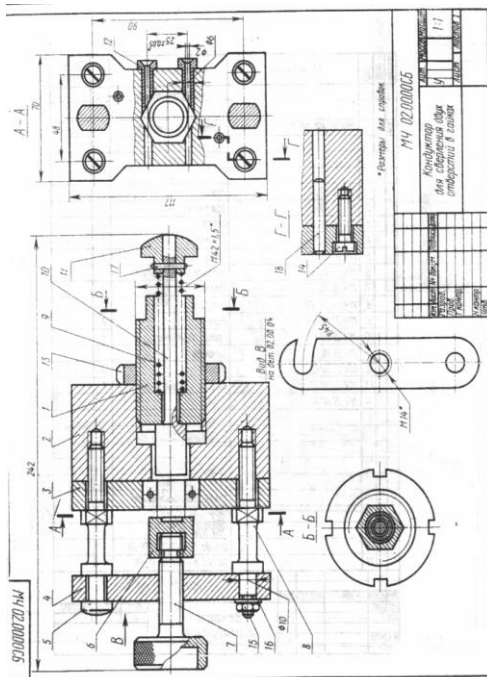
образец выполнения сборочного чертежа лист 3
